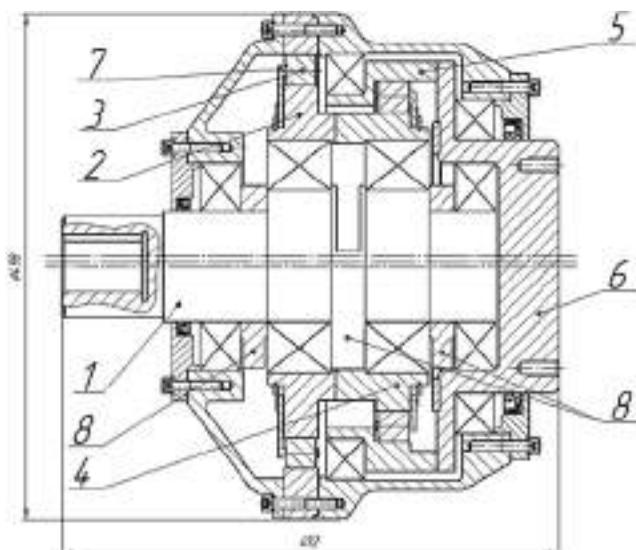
Компоновка привода на базе передачи ПТКиСО:
